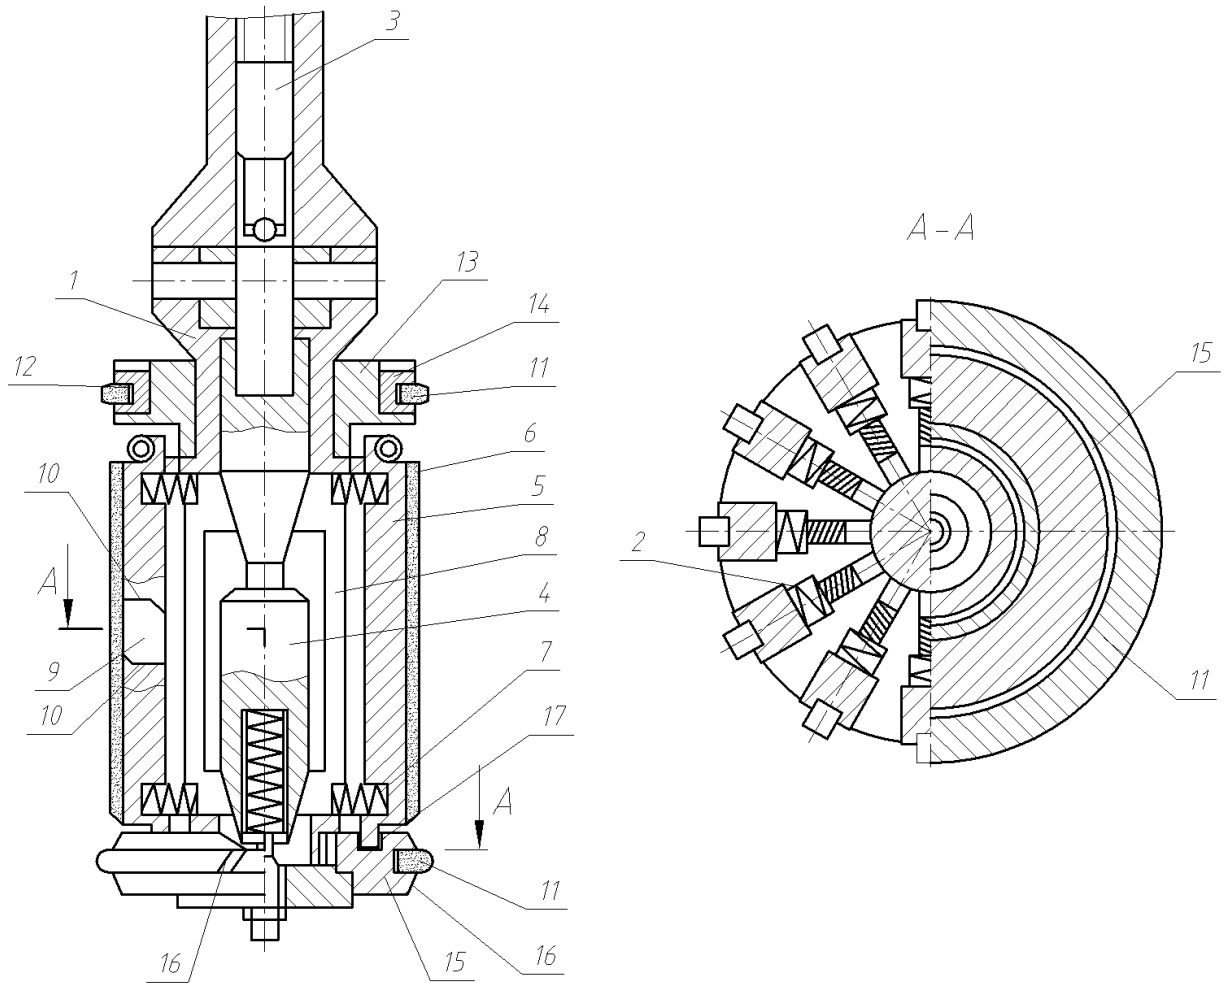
Конструкція хонінгувальної головки для шаржування поверхонь гільз циліндрів:
